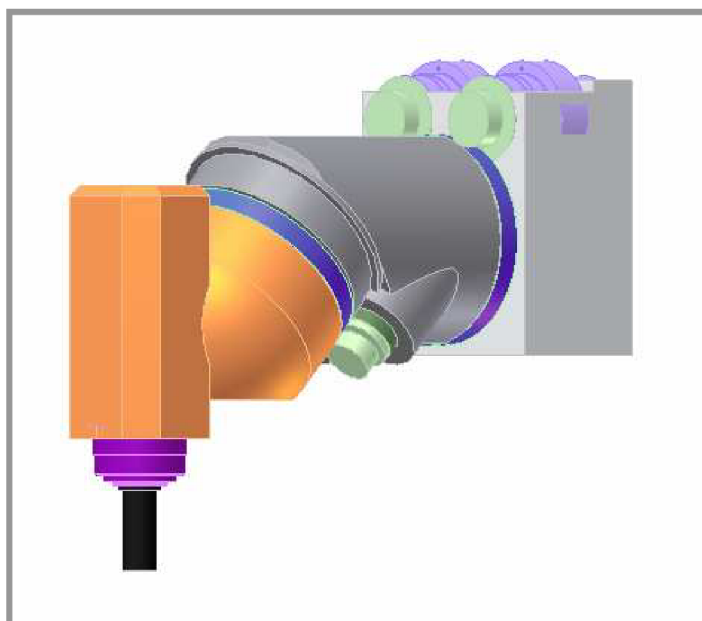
Univerzální frézovací hlava s motory umístěnými nad osou rotace C- 3D pohled
